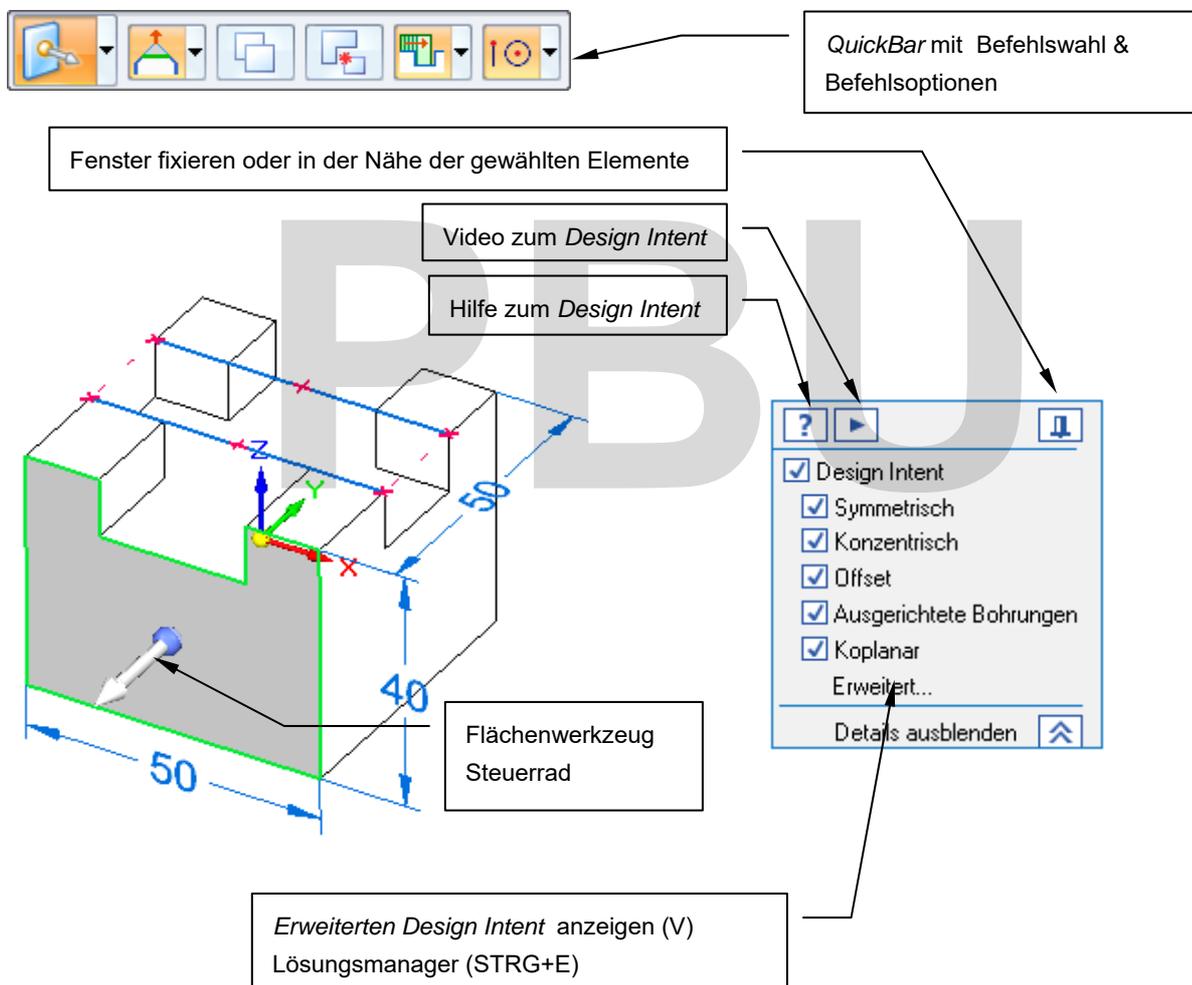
Gewählte Fläche mit *Design Intent*, Steuerrad und Bearbeitungswerkzeugen
